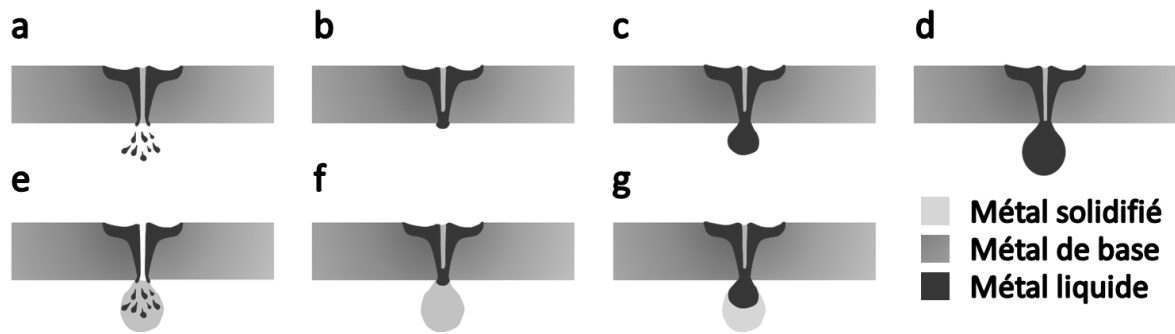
Mécanisme du dropping pendant le soudage hybride (vue en coupe de la zone de fusion)
